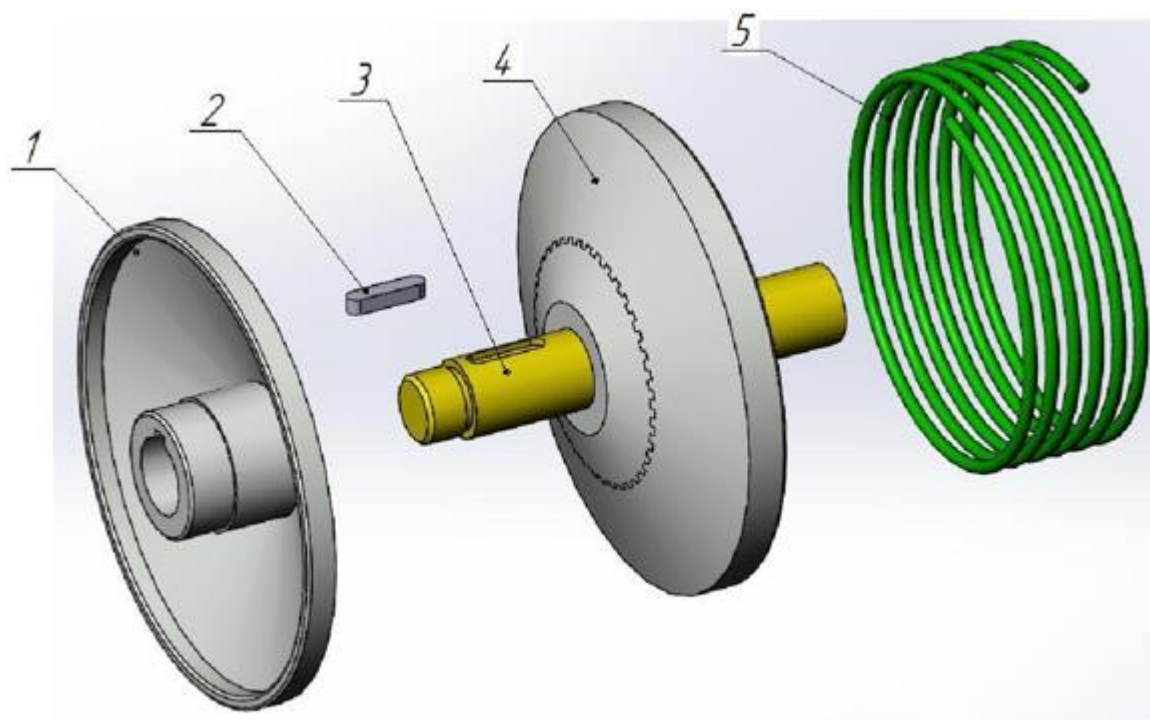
Ведомый шкив вариатора: 1 – неподвижная половина; 2 – шпонка; 3 – ведомый вал; 4 – подвижная половина; 5 – цилиндрическая пружина
